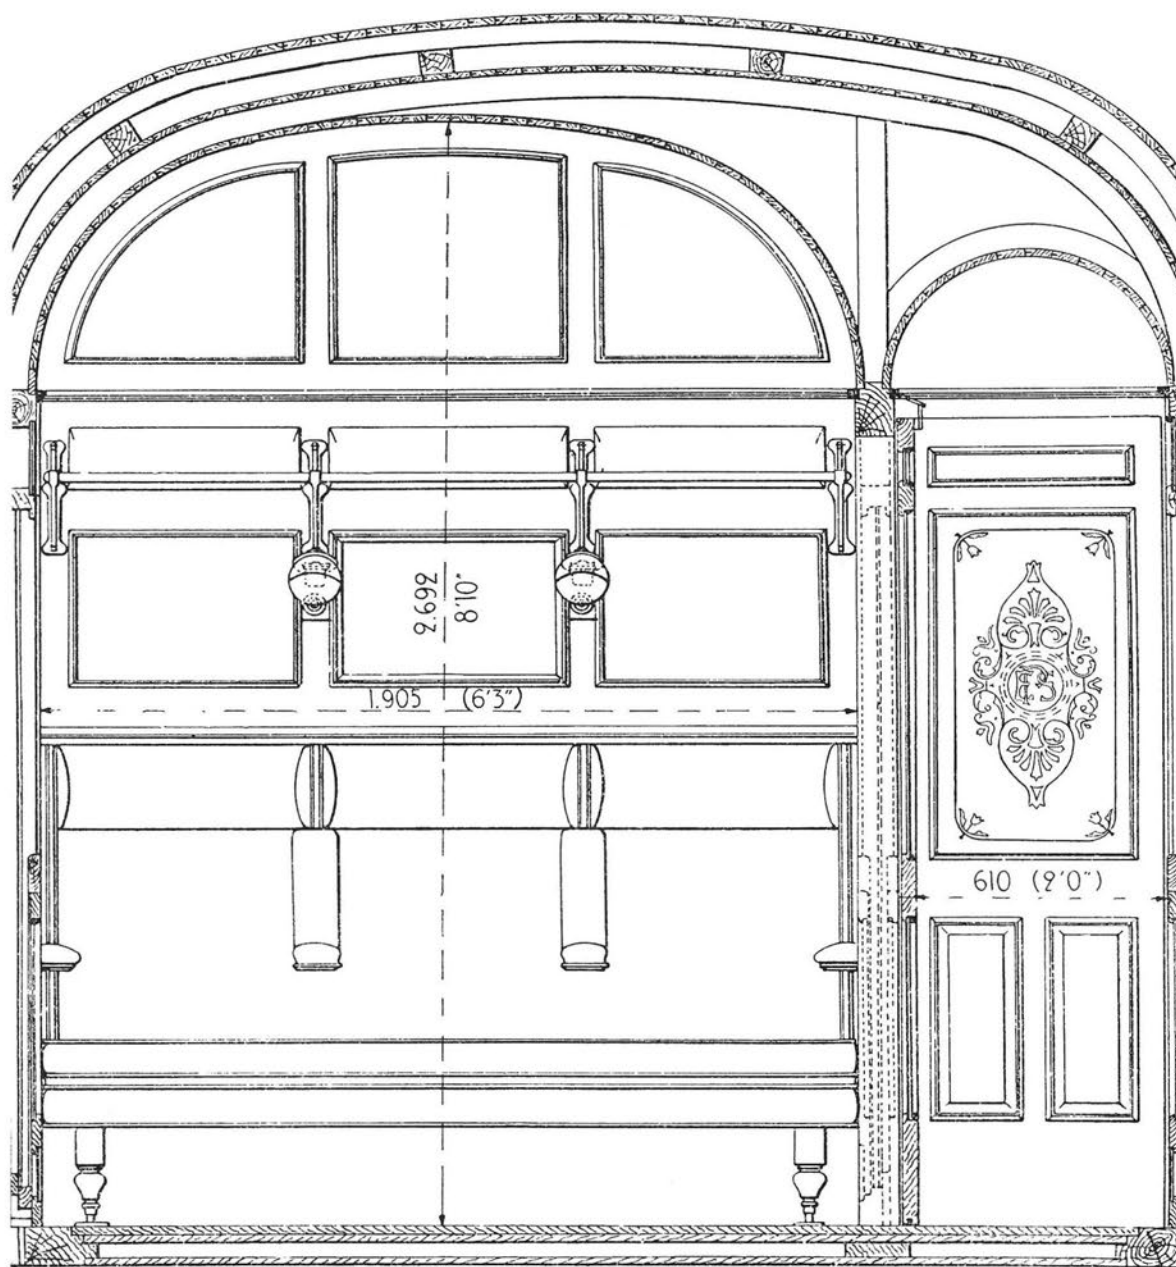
Coupe en travers des voitures récentes indiquant la disposition de la double toiture, des parois et des planchers.
